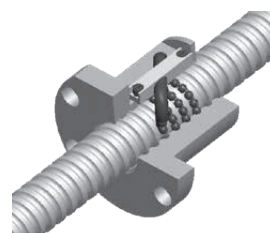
Kugelgewindemutter mit externer Kugelrückführung
